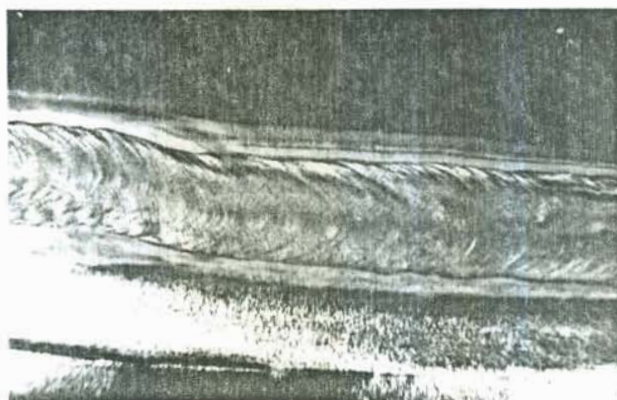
Desvio do cordão de solda quando o arco cruzou o ponto da conexão de retorno (terra).
